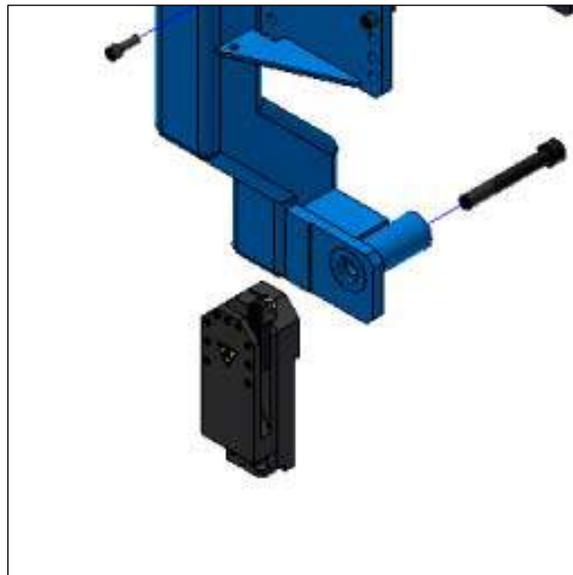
Einzelheiten zur Werkzeugkopf-Baugruppe
